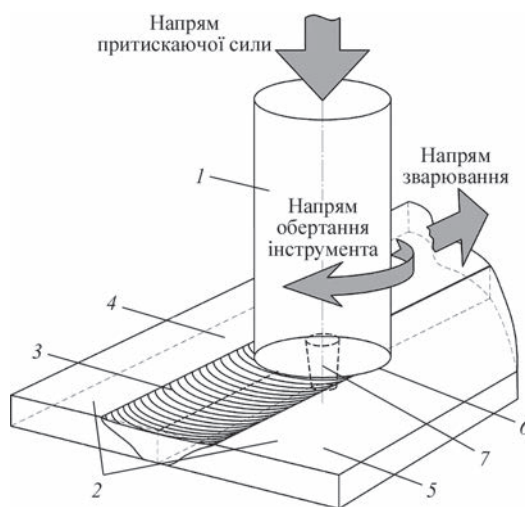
Процес зварювання двох пластин [1]: 1 — інструмент; 2 — пластини; 3 — зварний шов; 4 — сторона набігу інструмента; 5 — сторона повернення інструмента; 6 — заплечик; 7 — штир
